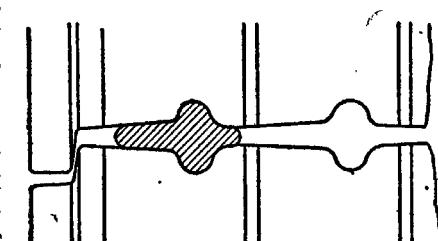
Расположение калибров на валках одной из клетей стана 250 для прокатки тавровой стали
